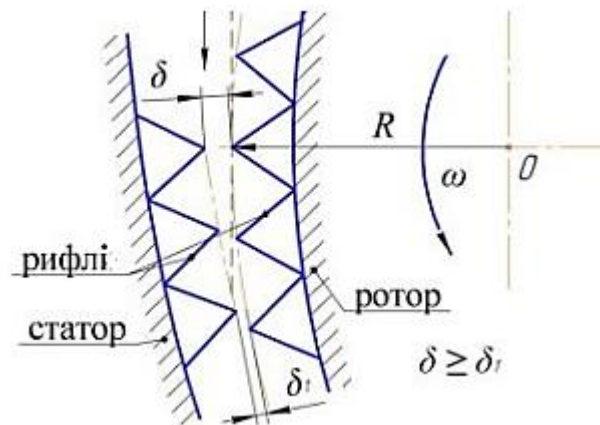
Схема взаємного розташування робочих поверхонь статора та ротора
